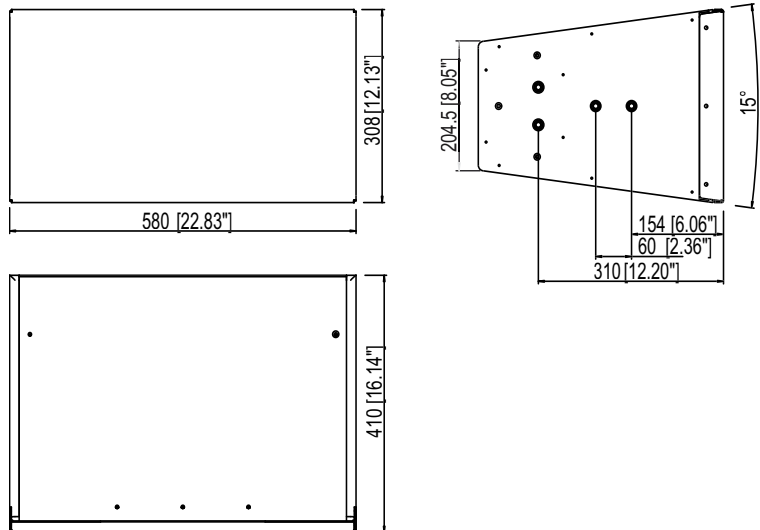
Qi10 dimensions du coffret en mm [inch]
